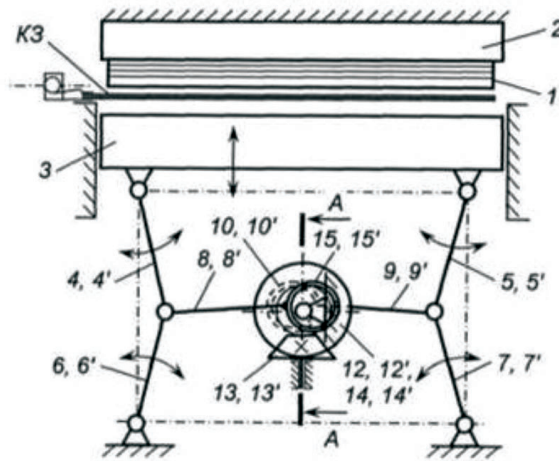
Плоский штанцювальний прес з механізмом привода натискної плити з конічними зубчастими колесами
